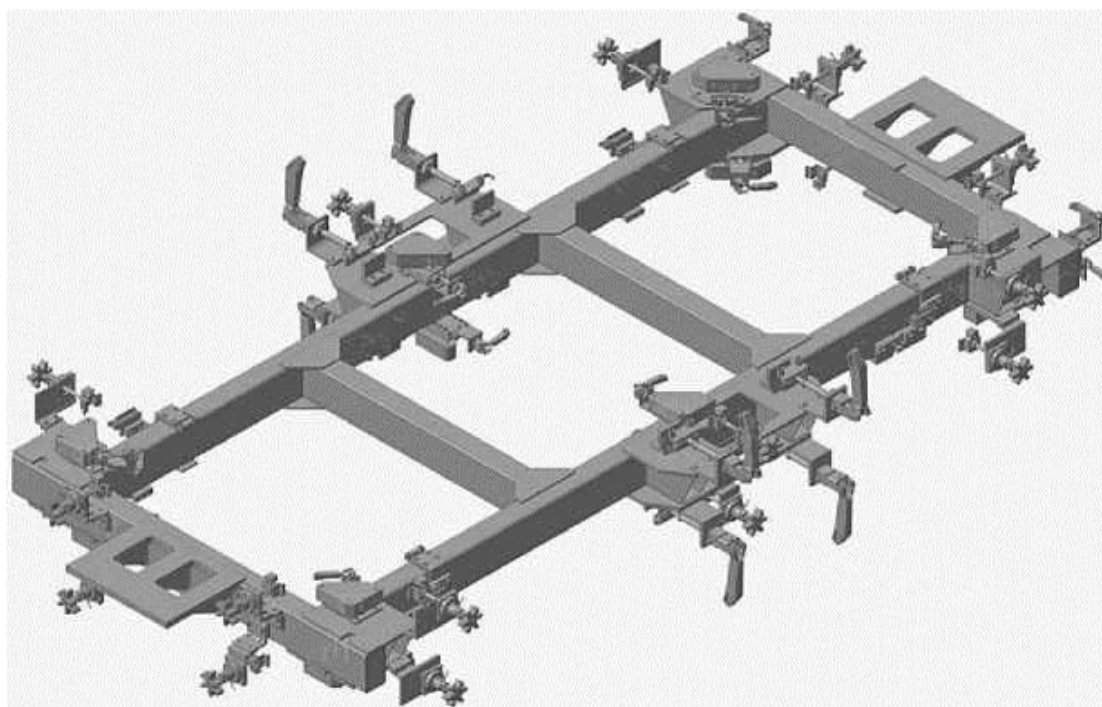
3Д модель пристосування для складання під зварювання
